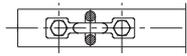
Ausführung für taschenverzahnte Kettenräder
